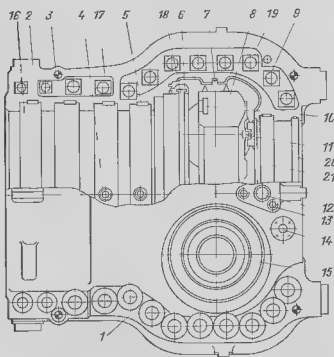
Внутренний корпус ЦВД (вид сверху):
